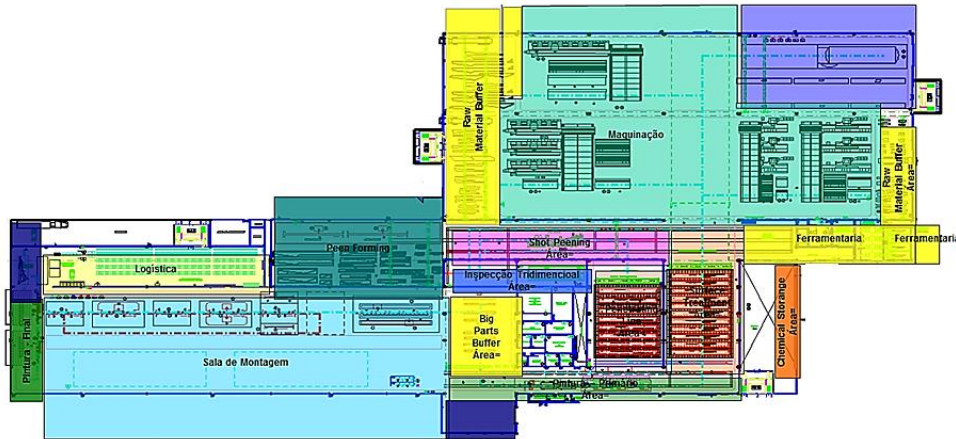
4 - Planta do hangar de Metálicas S.A.
